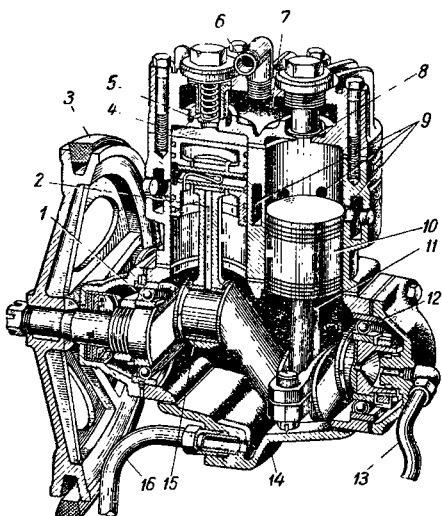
Компрессор пневматического привода тормозов автомобиля ЗИЛ-150.
